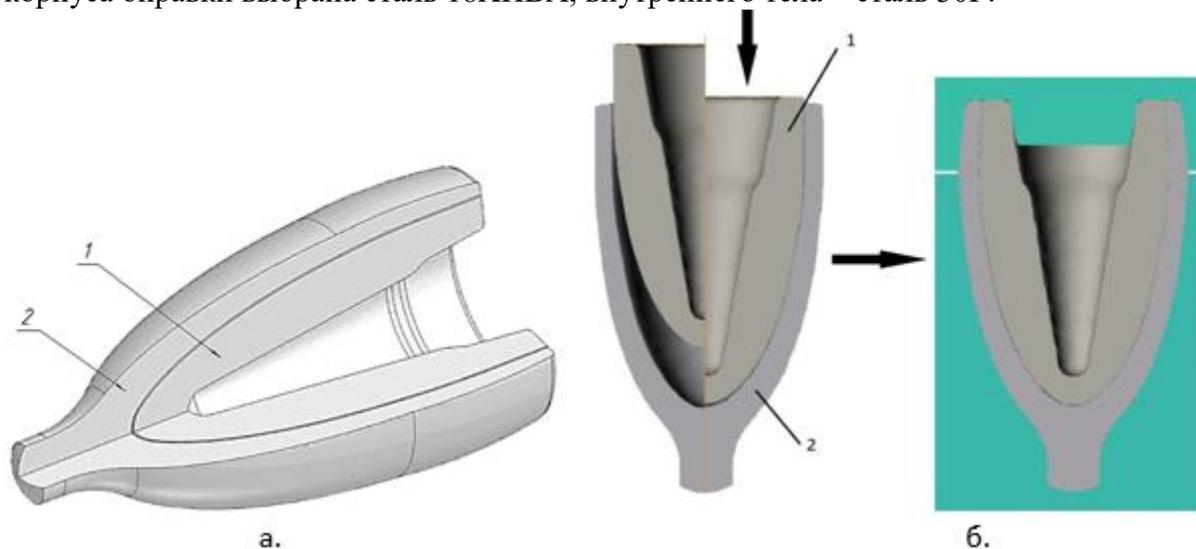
Двуслойная оправка косовалкового прошивного стана (а) и способ ее получения (б): 1 – внутреннее тело оправки; 2 – наружный корпус оправки.
